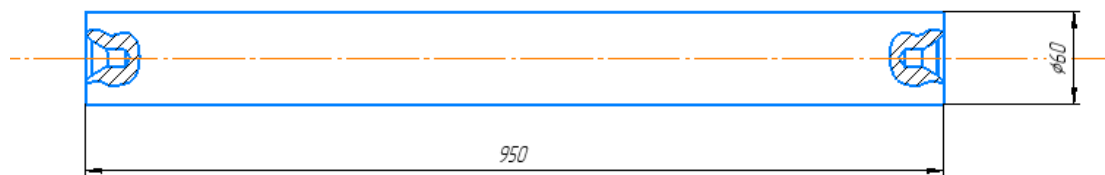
Операція 010 (фрезерно - центрувальна)
